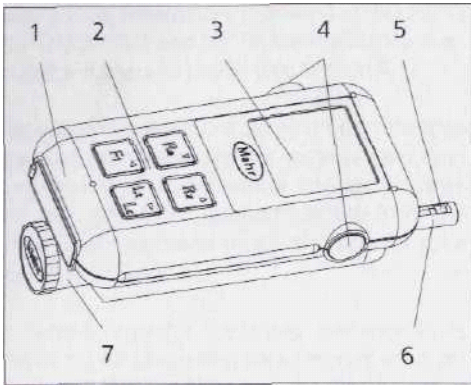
Измерительный прибор для измерения шероховатости MarSurf PSI
